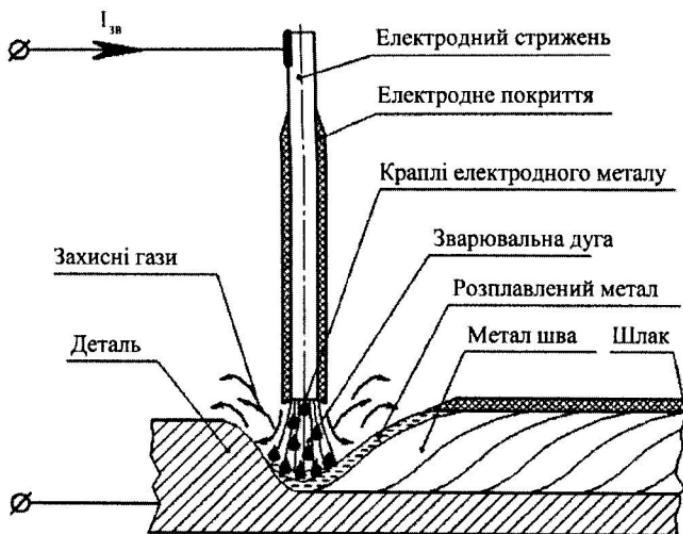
Схема ручного дугового зварювання покритим електродом
